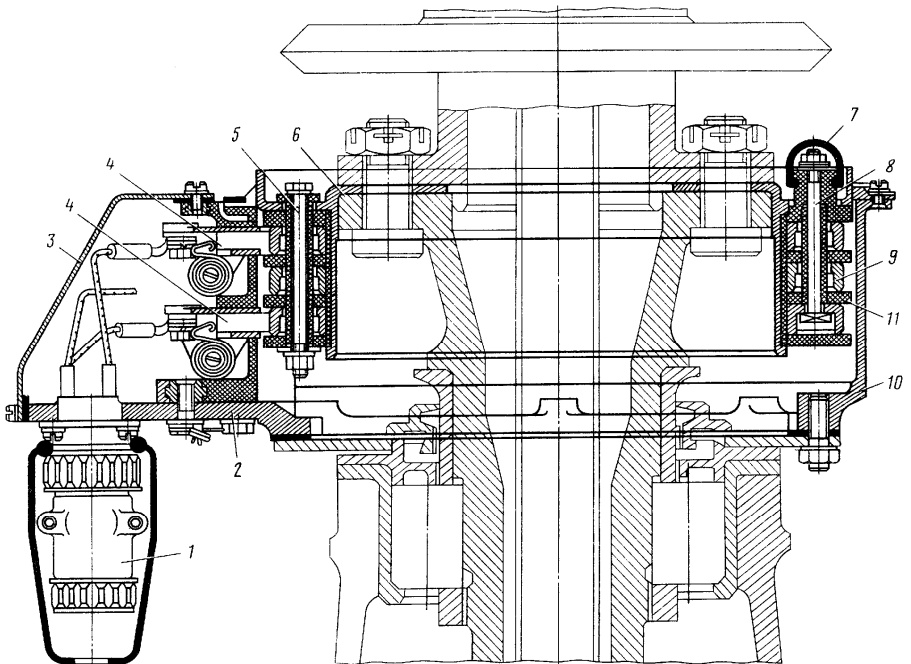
Токосъемник рулевого вента: 1 – штепсельный разъем; 2 – щеточная колодка; 3 – крышка; 4 – щетка марки МГСО; 5 – стяжной болт; 6 – коллектор; 7 – резиновый чехол; 8 – контактный болт; 9 – контактное кольцо; 10 – корпус токосъемника; 11 – изоляционное кольцо
